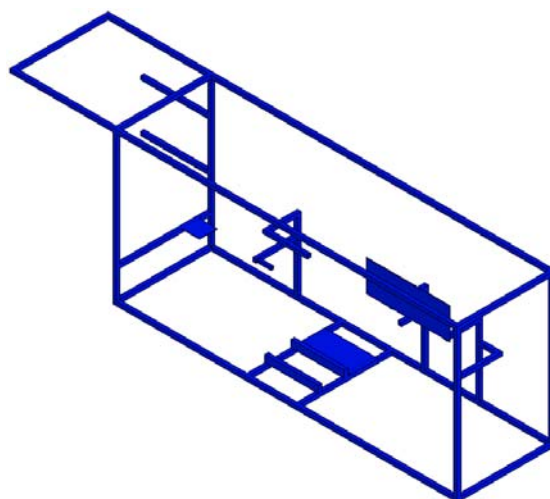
Estructura diseñada para el soporte de los elementos de la planta piloto
